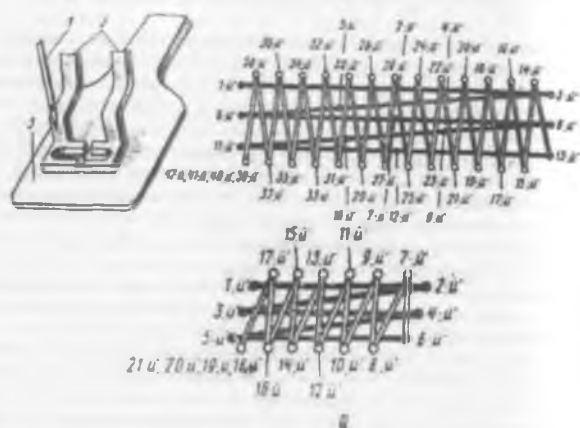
Изготовление малой (а) и большой (б) закрепок
